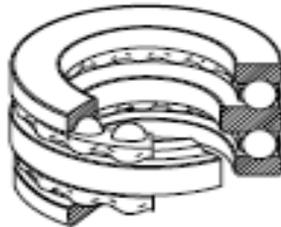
Rodamientos de bolas de apoyo axial de doble dirección
